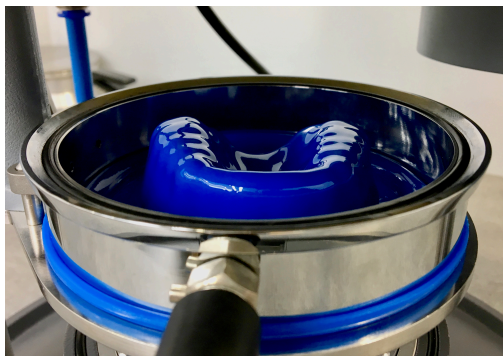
Ouverture de la thermoformeuse et PIB obtenue après thermoformage
